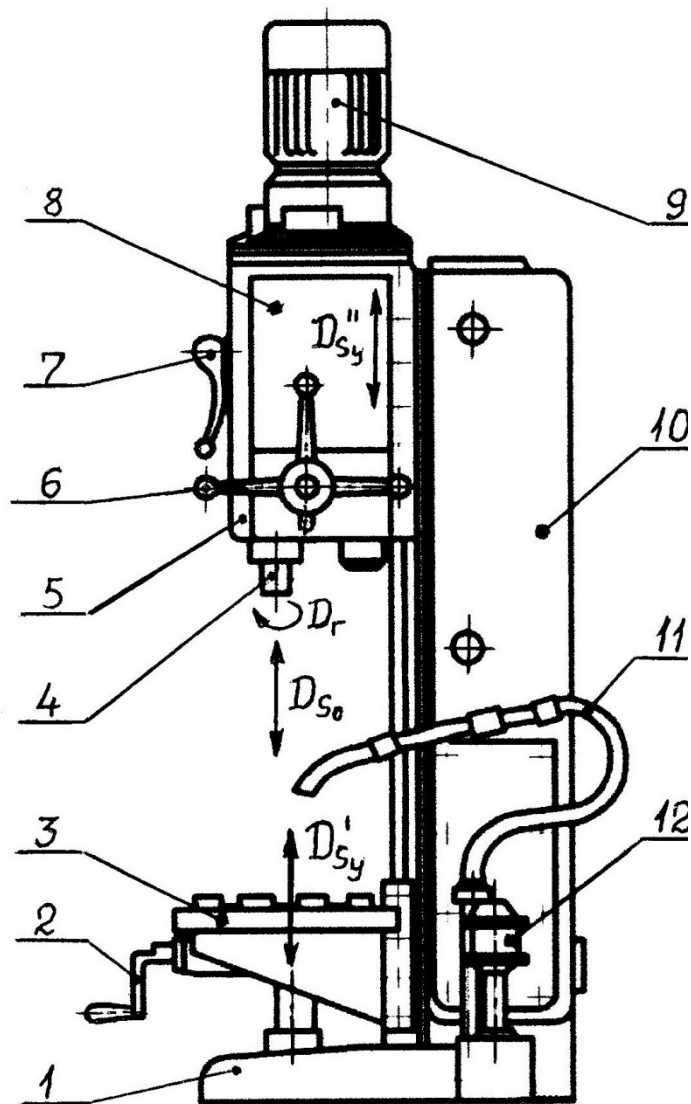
Общий вид вертикально-сверлильного станка:
